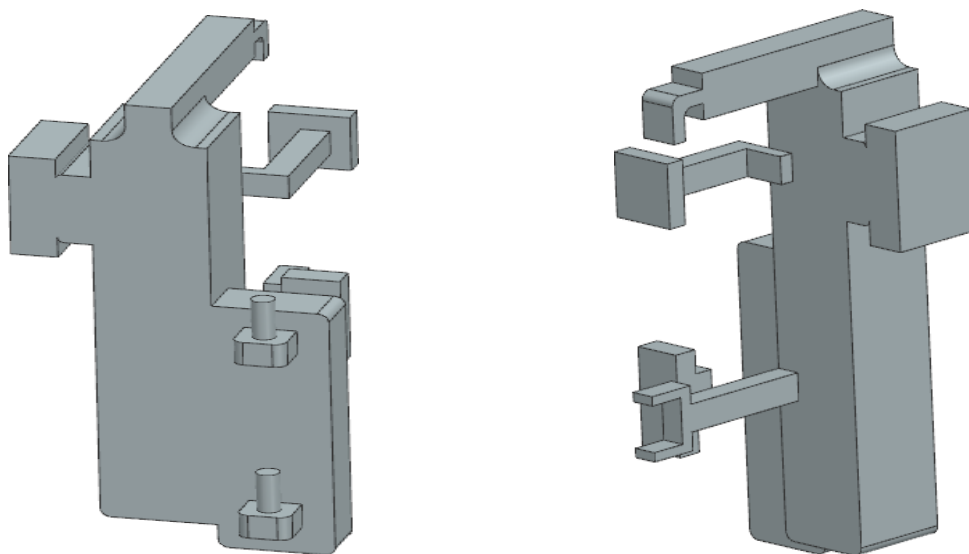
y 40. Diseño en CAD del diseño de la base.
